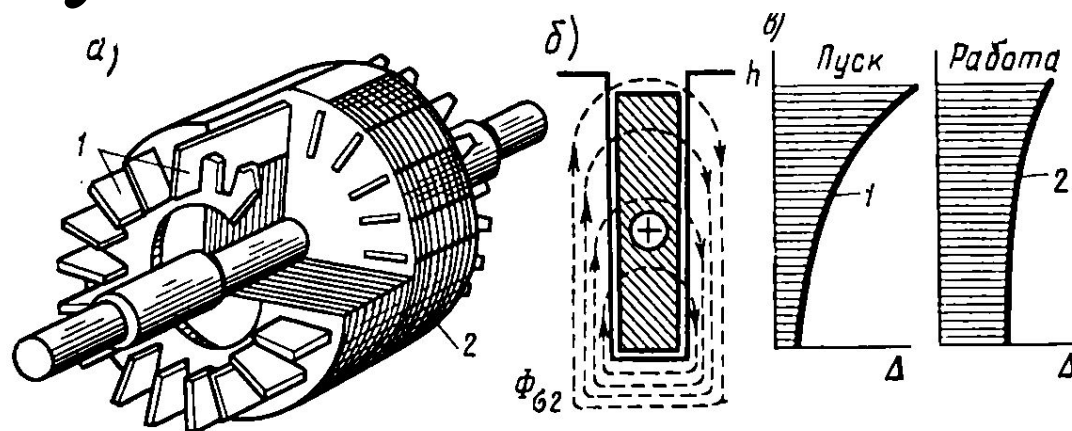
Общий вид (а), разрез паза (б) ротора глубокопазного двигателя и разновидности пазов глубокопазных двигателей (в):
